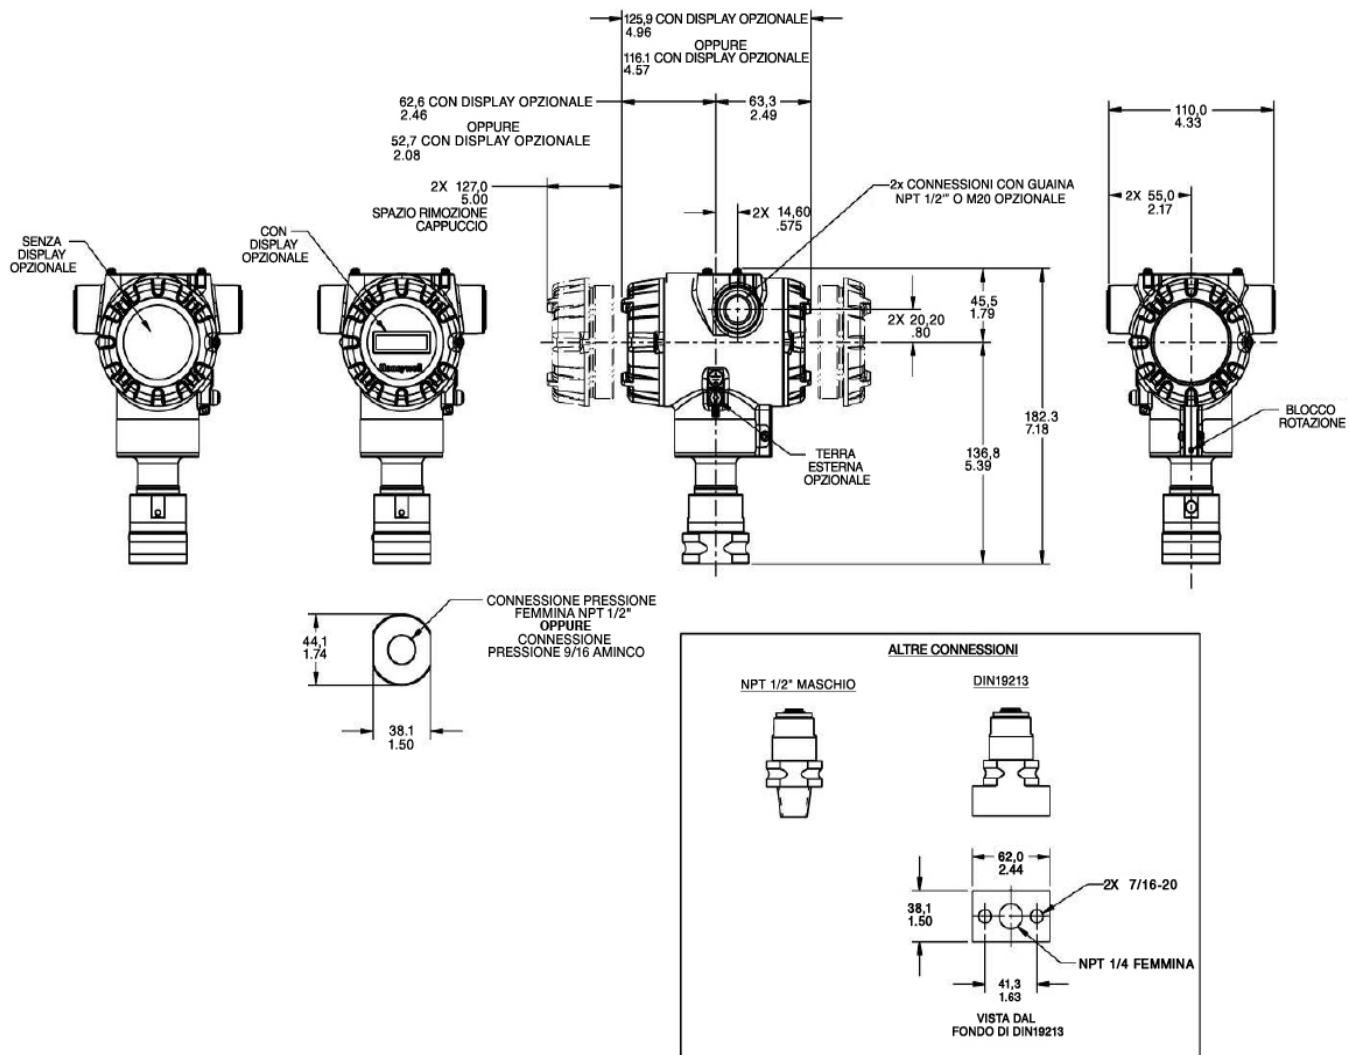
Dimensioni di montaggio tipiche di STA72L, STA74L e STA77L per riferimento
